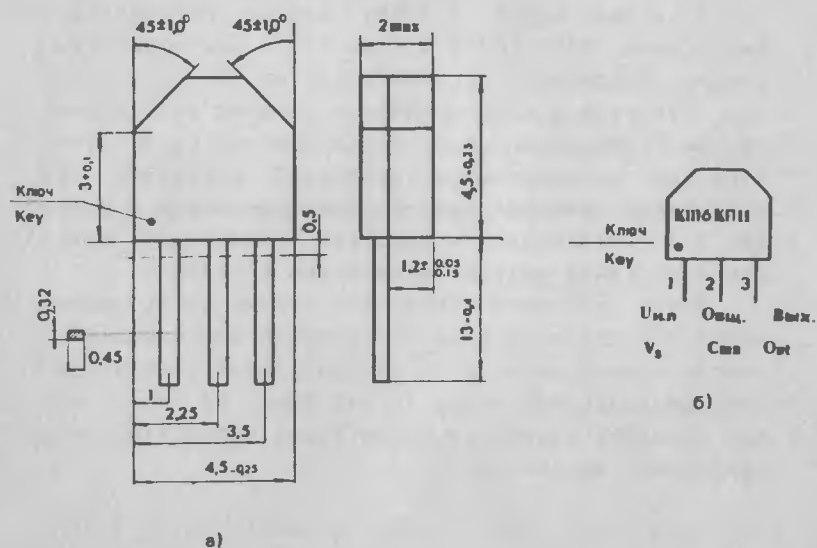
Микросхема К1116КР11: а - корпус; б - цоколевка.
